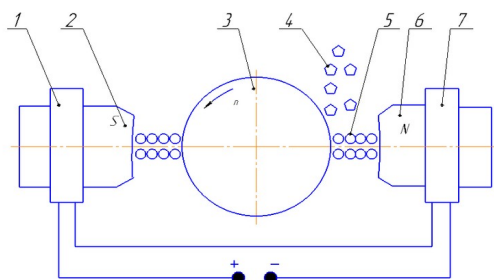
Схема магнитно-абразивной обработки наружных поверхностей, где: 1 и 7 – магнитопроводы электромагнитной системы; 2 и 6 – полюса; 3 – обрабатываемая деталь; 4 – подаваемый ферроабразивный порошок; 5 – цепочки ферроабразивного порошка
